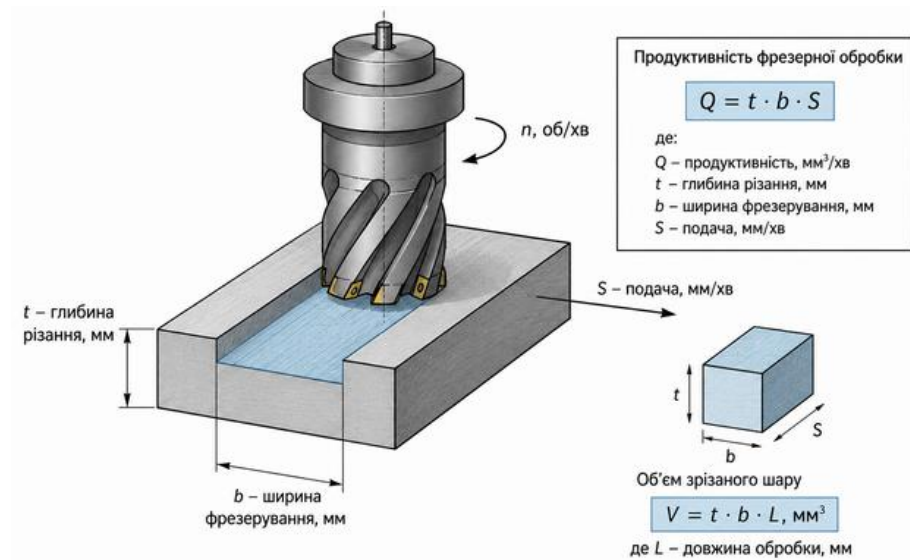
Схема визначення продуктивності фрезерної обробки[15]
